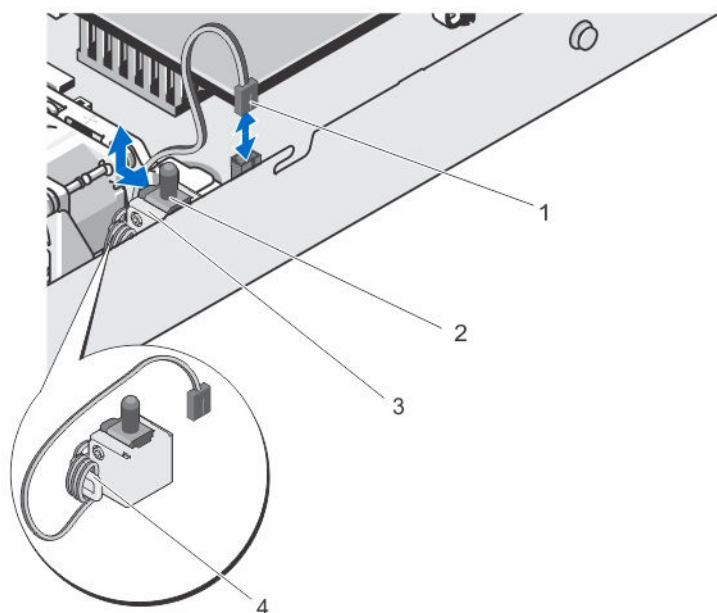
Entfernen und Installieren des Gehäuseeingriffschalters
